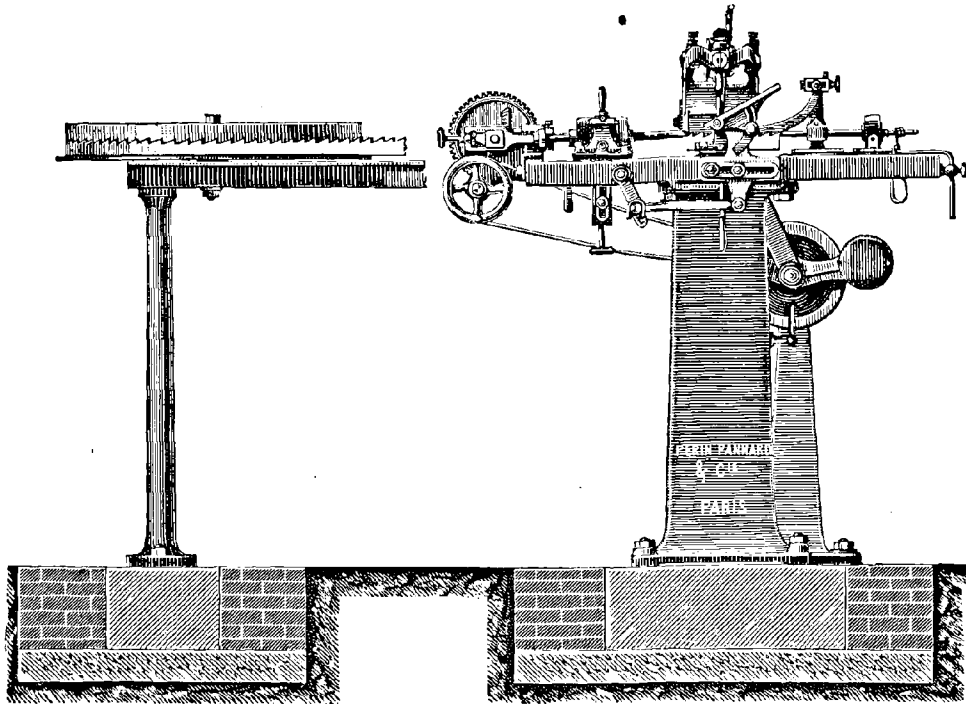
Machine automatique à affûter les scies à ruban. — Vue de face.
